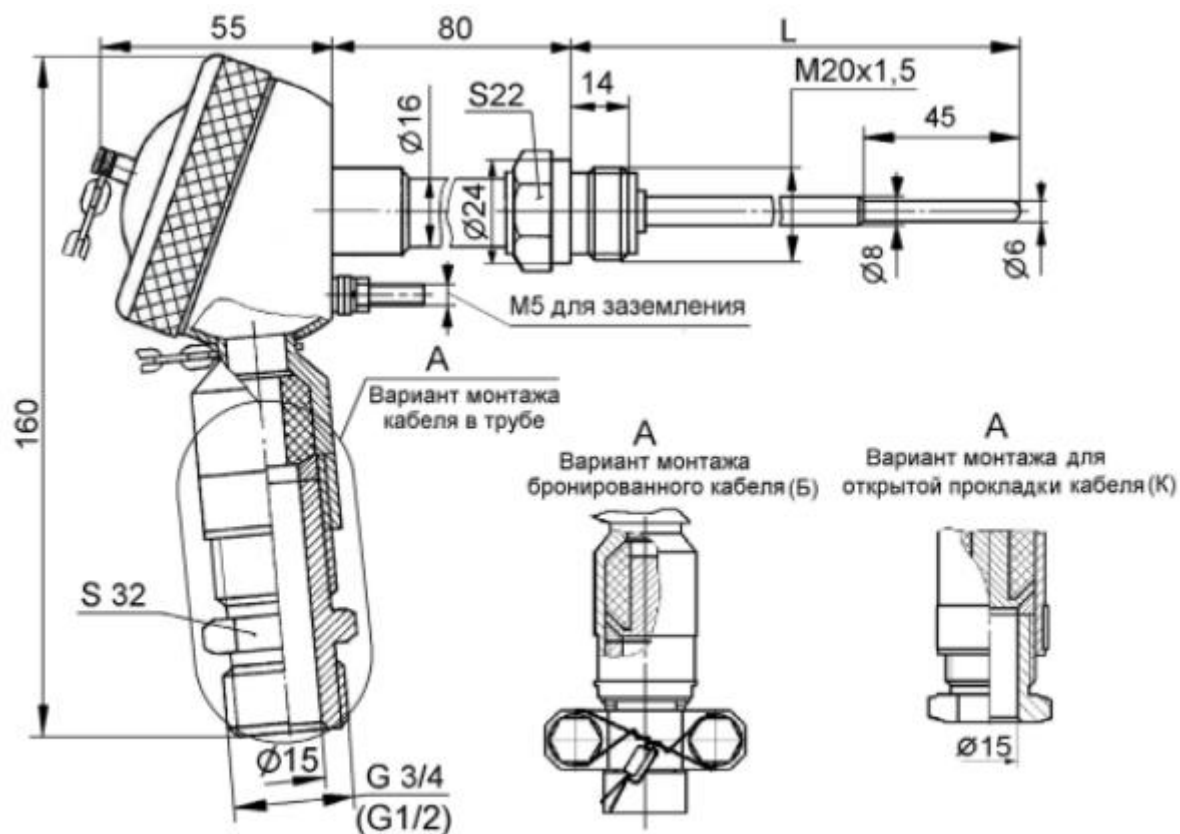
Головка из нержавеющей стали, штуцер неподвижный
